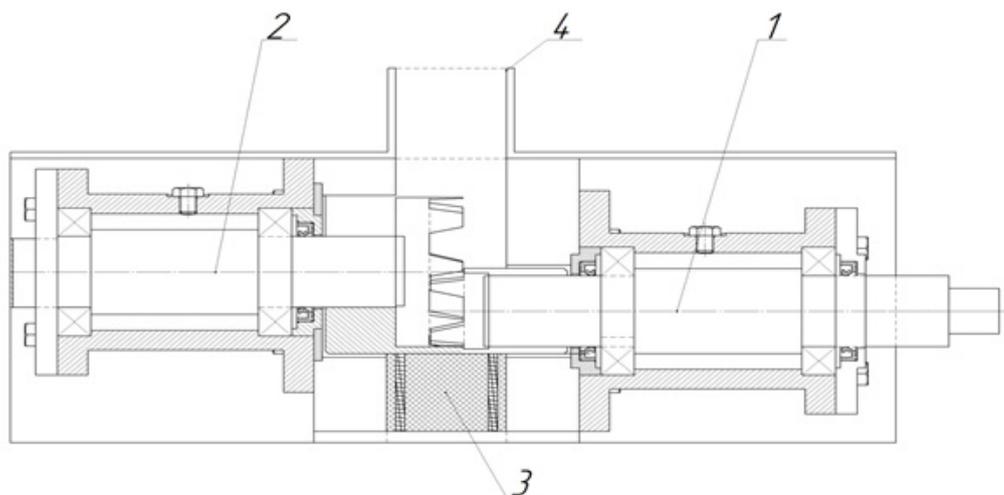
Схема устройства для получения древесной муки из отходов лесозаготовок:
